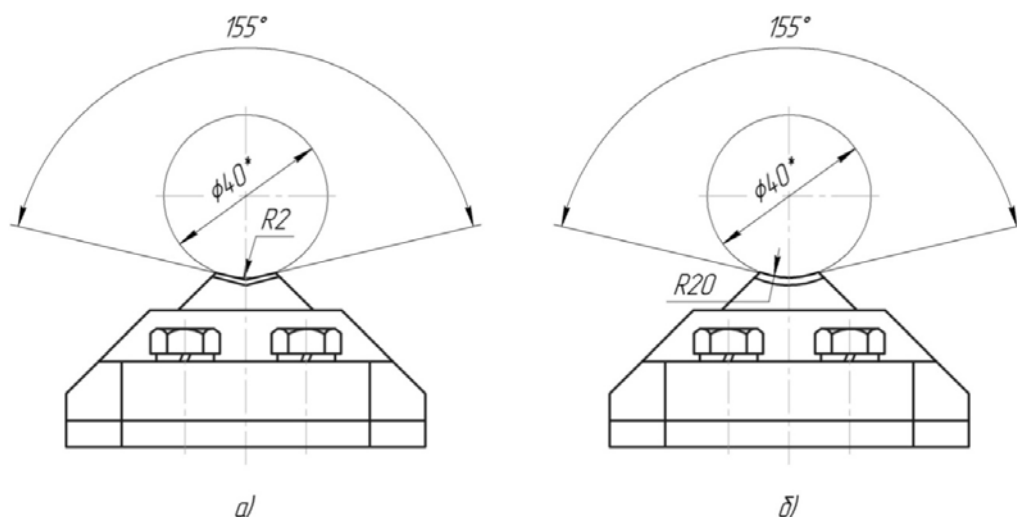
Бойки для обжатия с одинаковым углом охвата заготовки $\theta = 155^\circ$:
